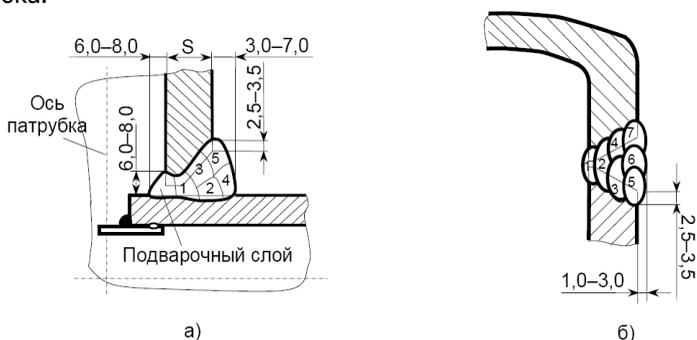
Последовательность сварки ложного штуцера: а – сварка патрубка с ремонтируемым изделием; б – сварка патрубка с дном; S – толщина патрубка
